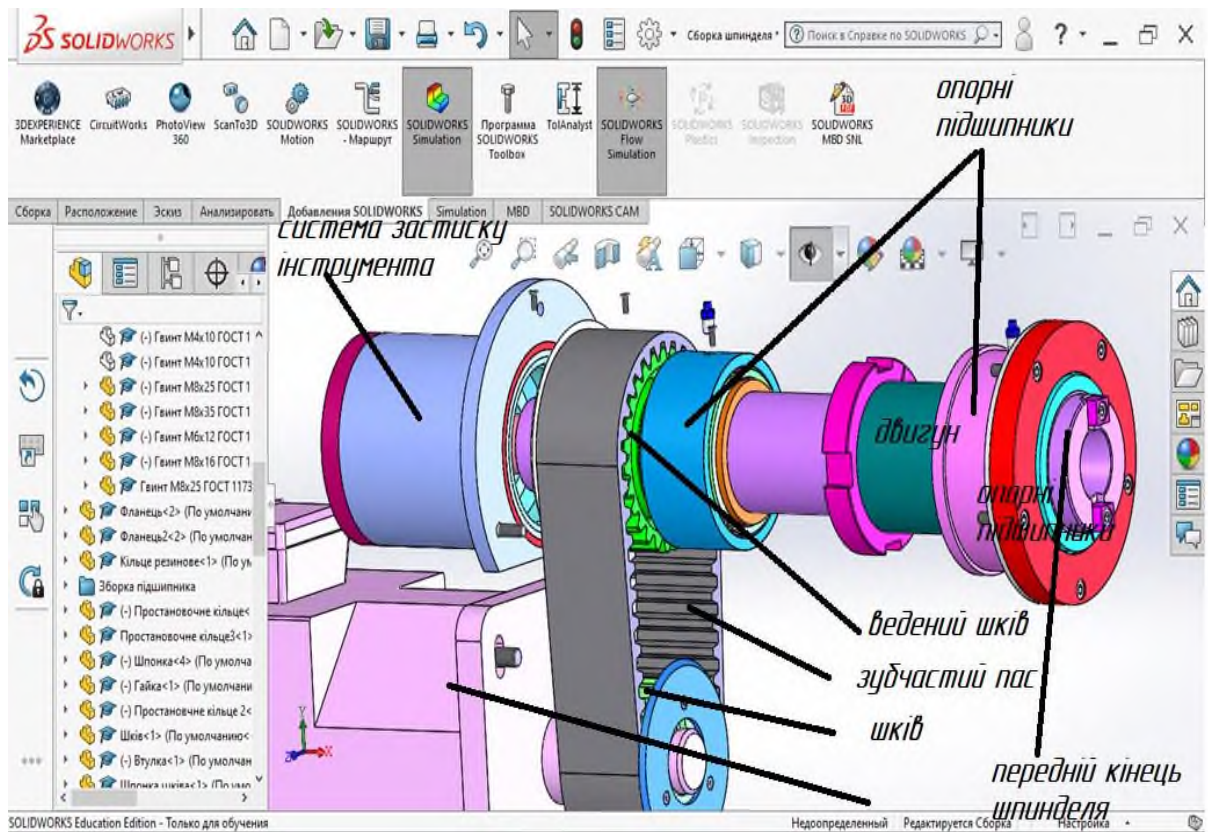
CAD-модель шпиндельного вузла вертикально-фрезерного верстата
